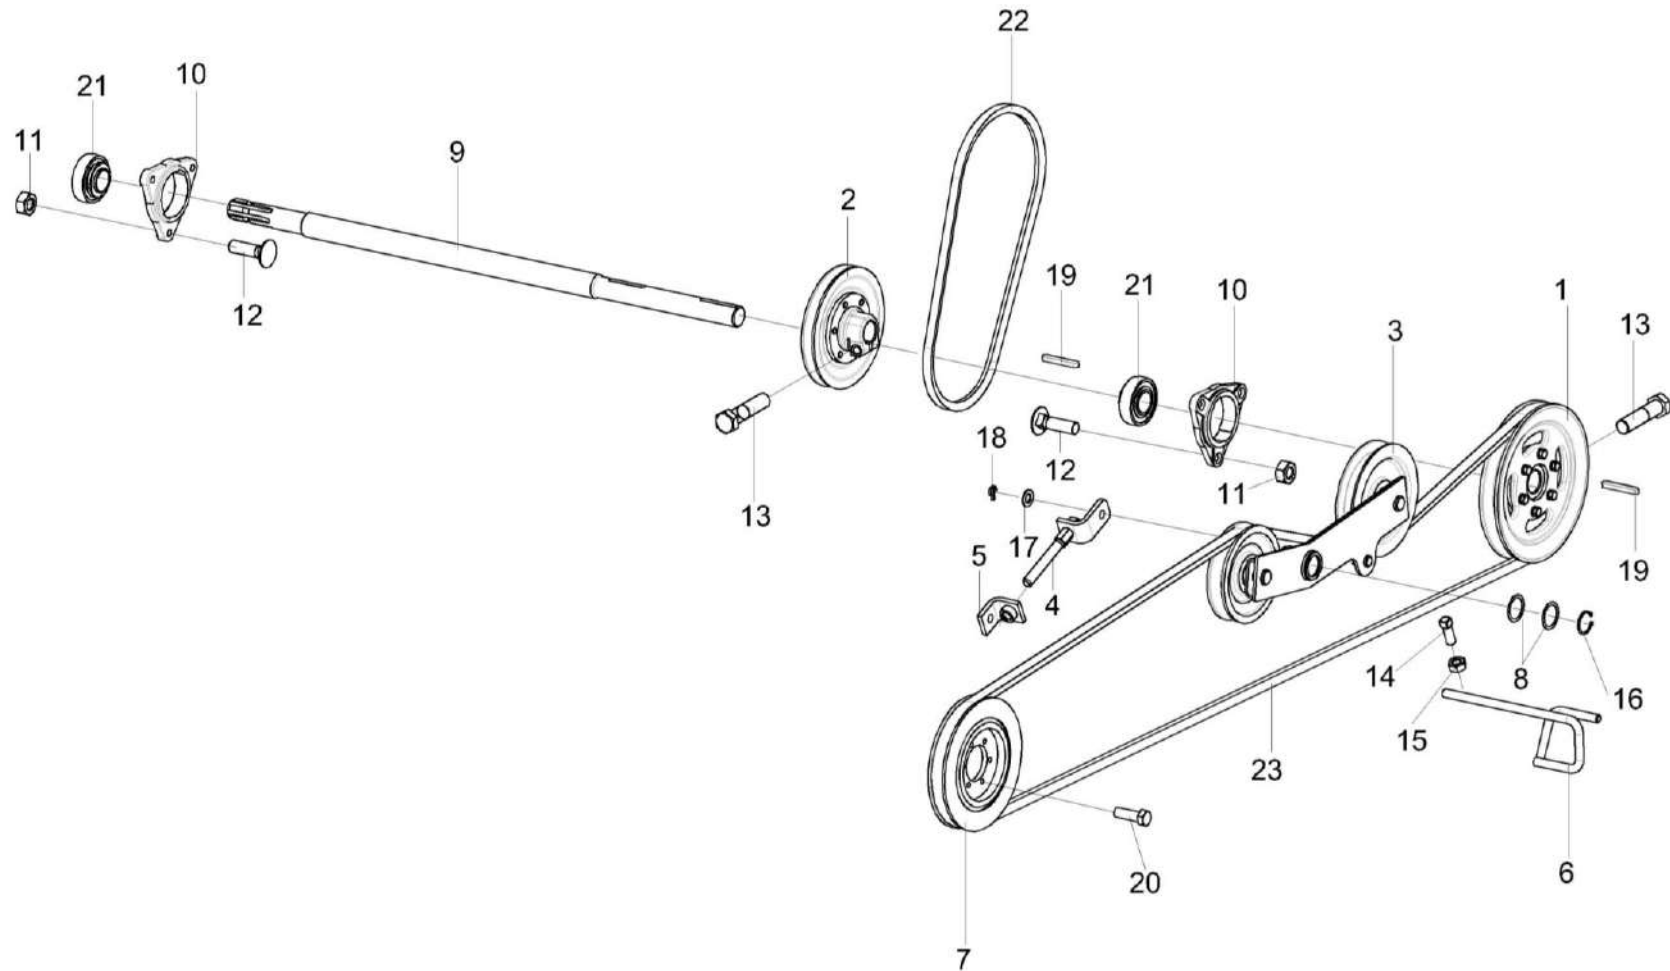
Установка привода режущего аппарата ЖТ-9-1504100Б
